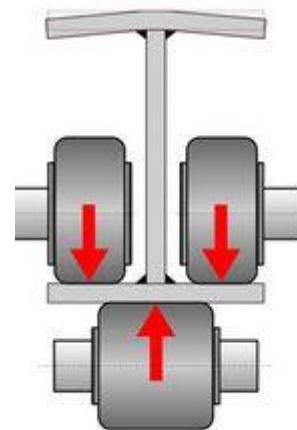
Правильний верстат Bendmak BPS500 [25]
